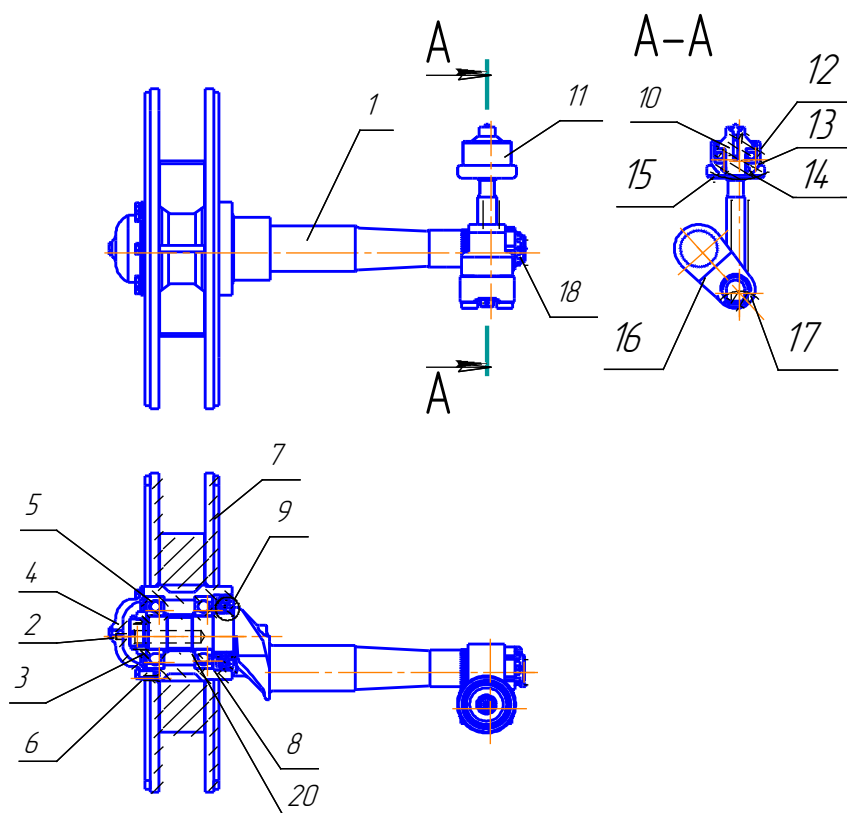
Направляющее колесо с натяжным механизмом:
